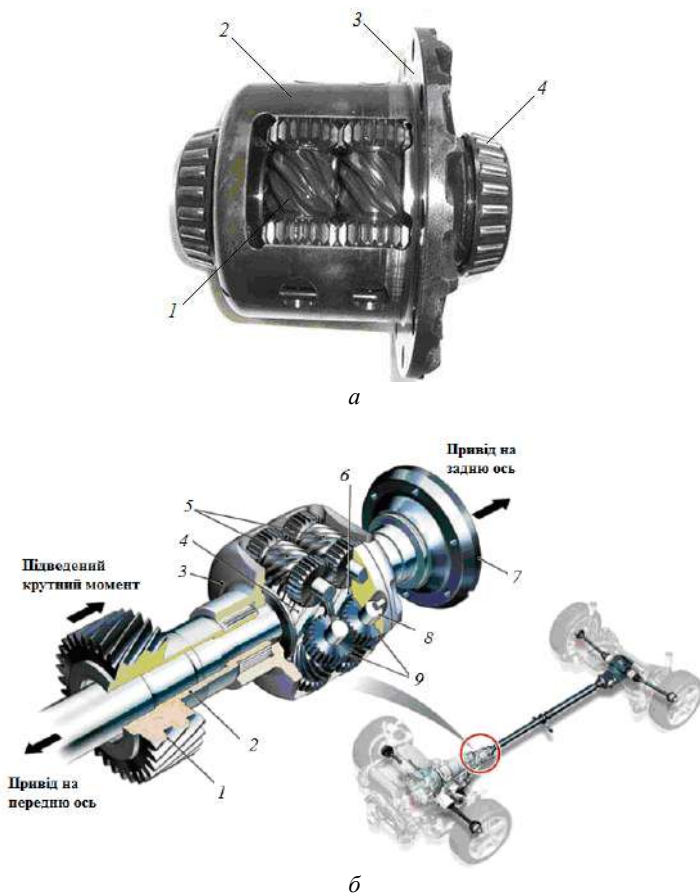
Диференціал Torsen T1: *a* – натуральний вид: 1 – сателіт; 2 – корпус; 3 – фланець кріплення веденої шестерні головної передачі; 4 – підшипник корпусу; *б* – зв’язок між елементами конструкції: 1 – ведуча шестерня; 2 – полий вал; 3 – корпус диференціала; 4 – сонячна шестерня приводу передньої осі; 5 – черв’ячні шестерні; 6 – сонячна шестерня приводу задньої осі; 7 – фланець валу приводу задньої осі; 8 – вісь черв’ячної шестерні; 9 – сателіти
